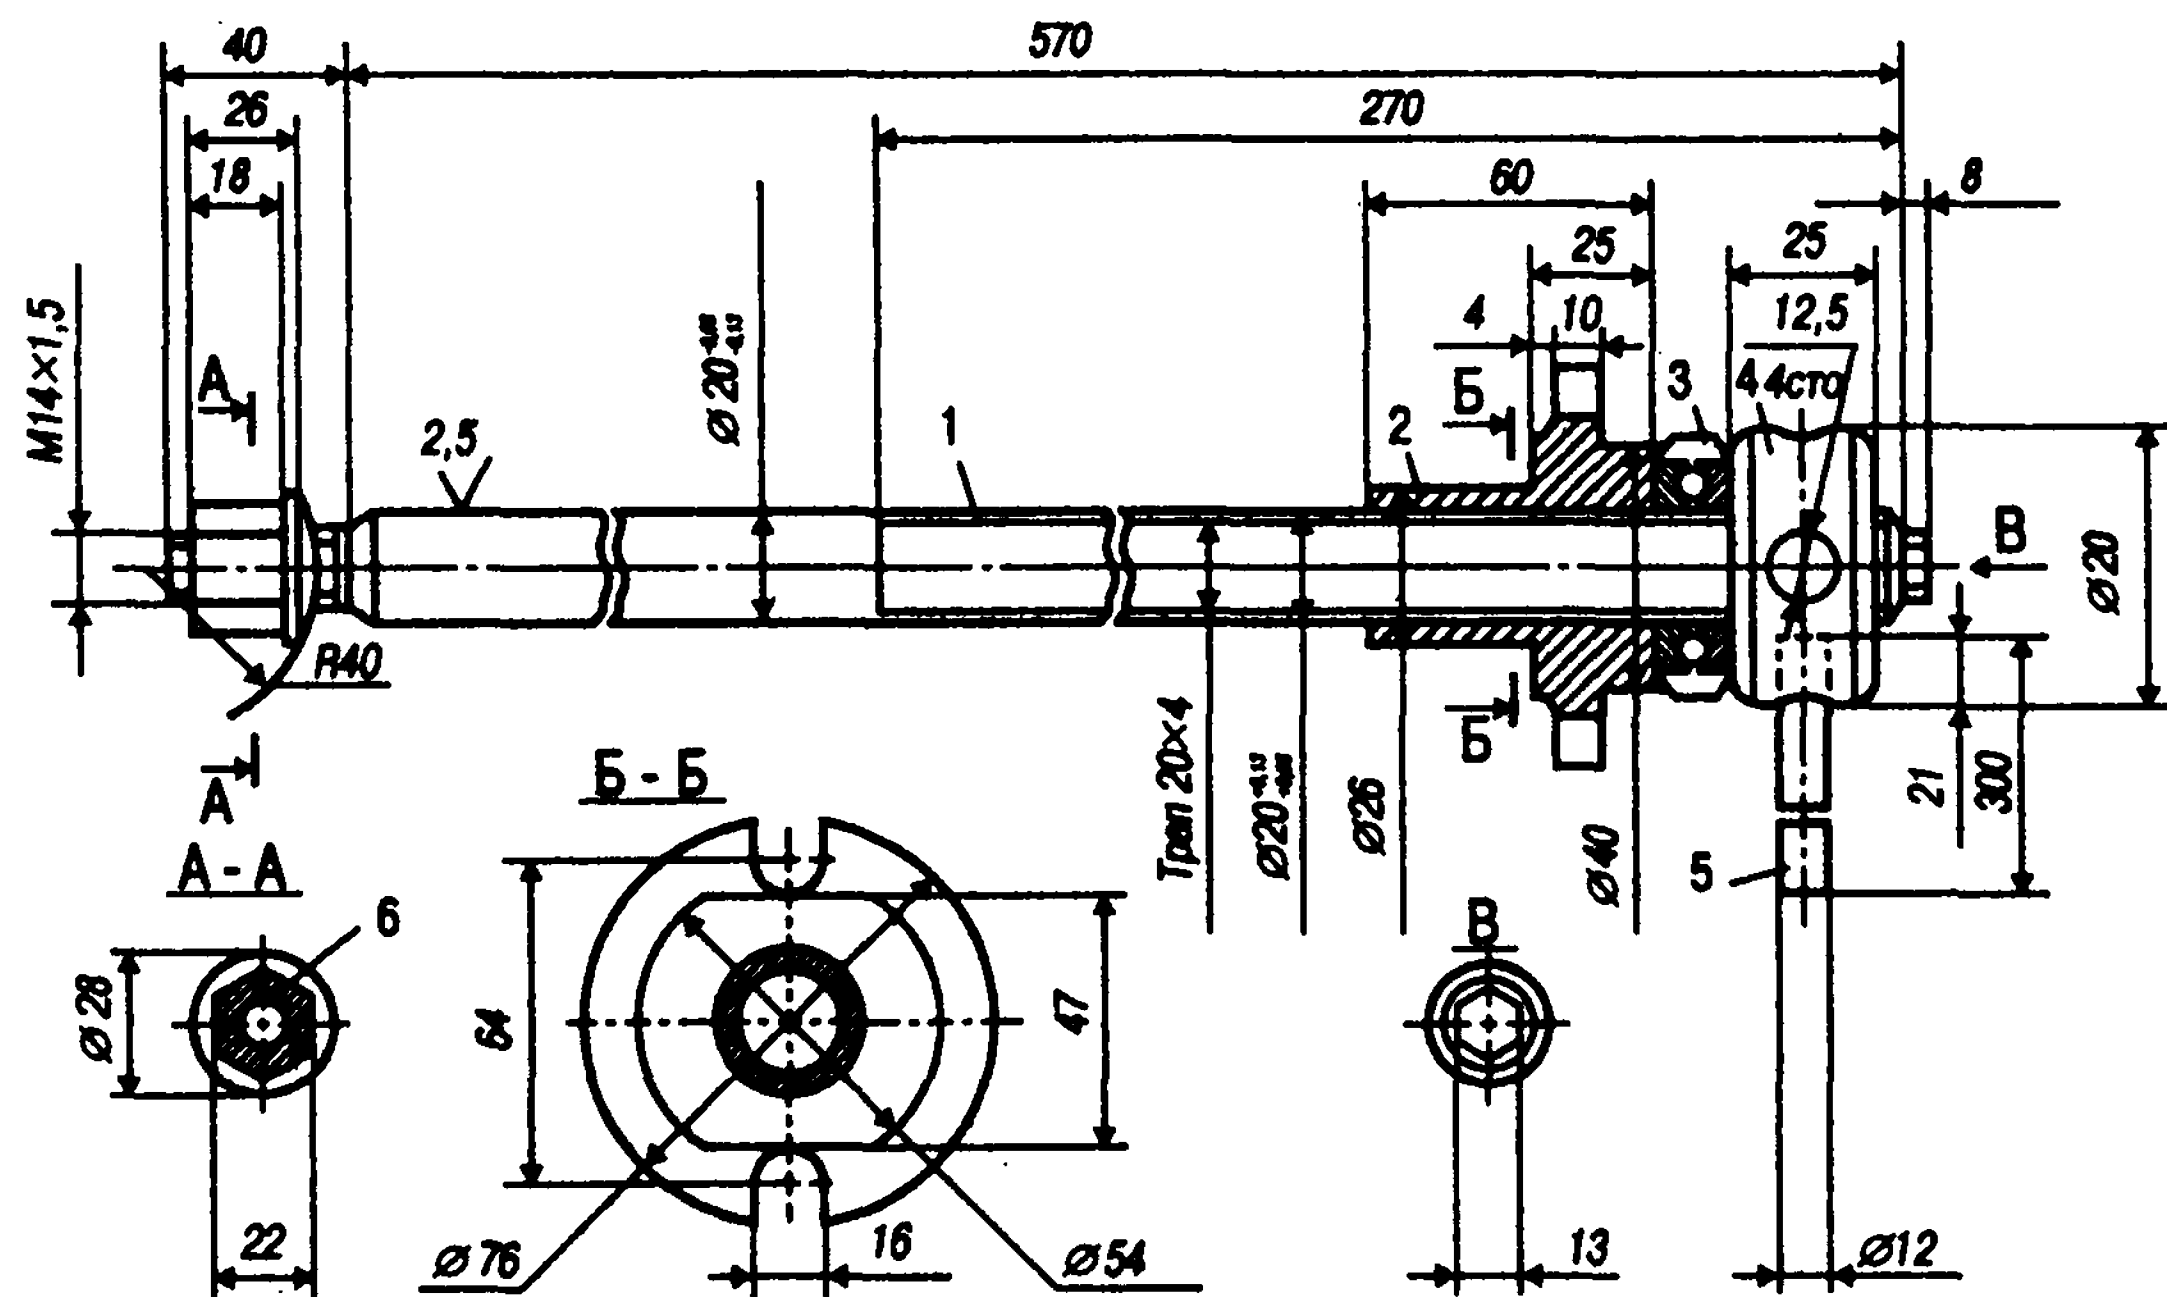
Приспособление для снятия пружины передней подвески: 1 - винт; 2 - фланец; 3 - упорный подшипник; 4 и 6 - гайки; 5 - рукоятка
